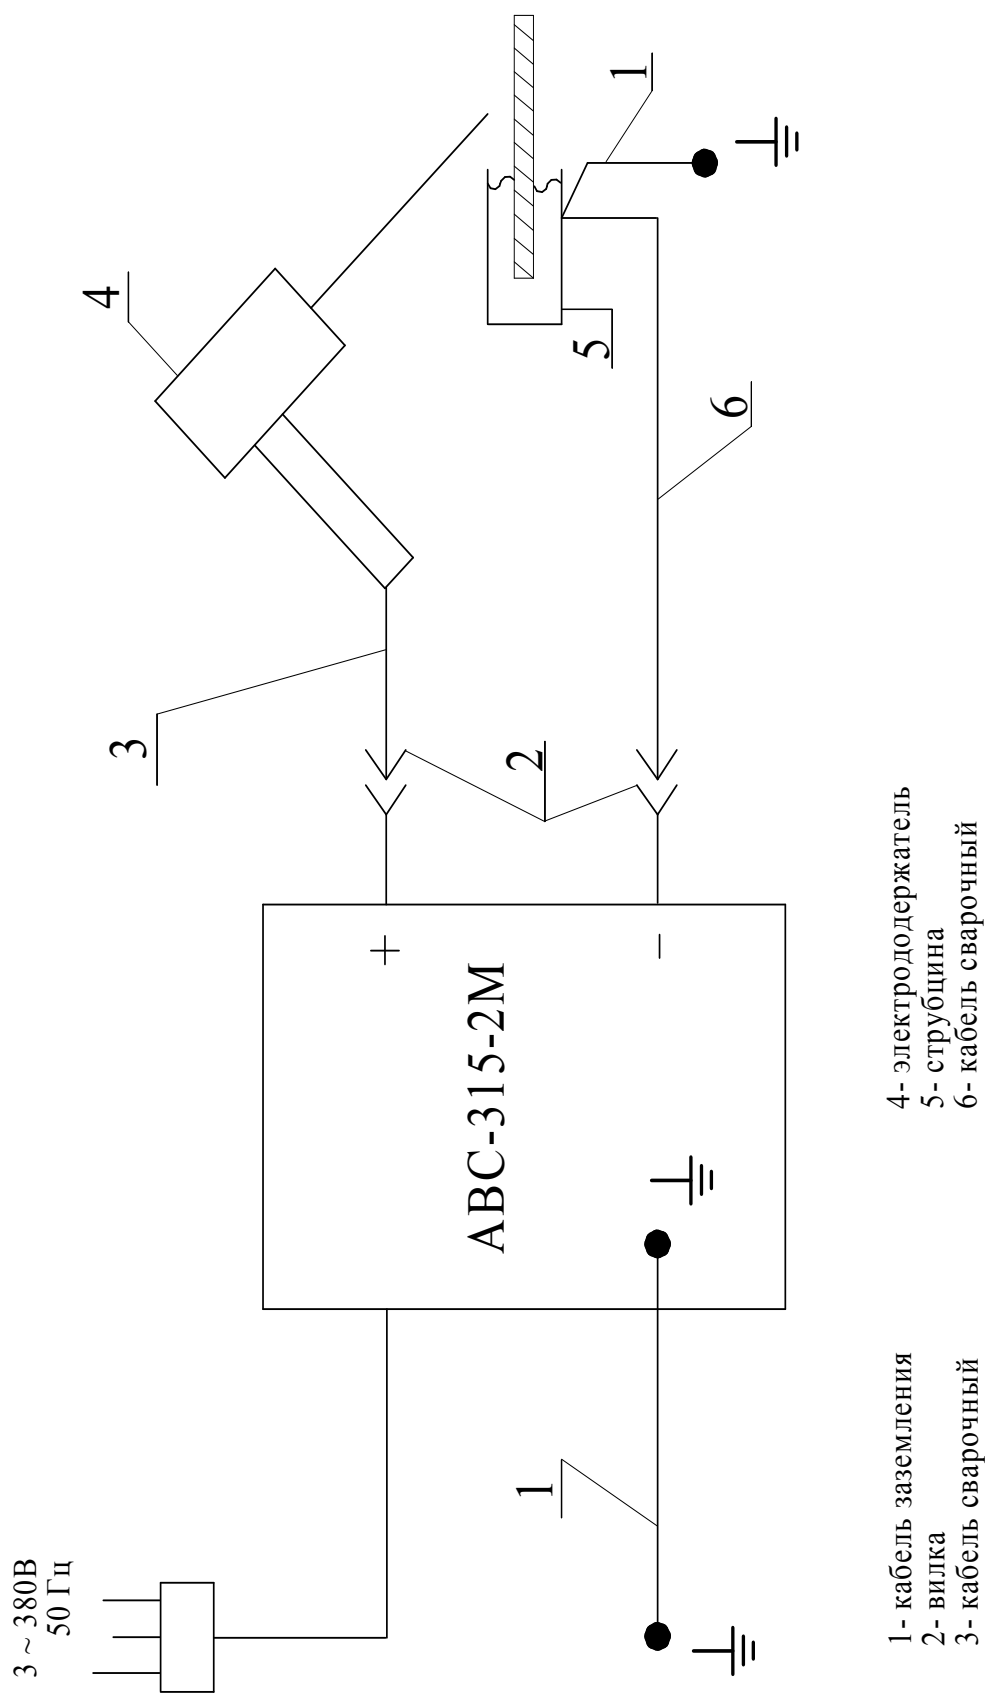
Схема рабочего места для ручной дуговой сварки аппаратом ABC-315-2M
